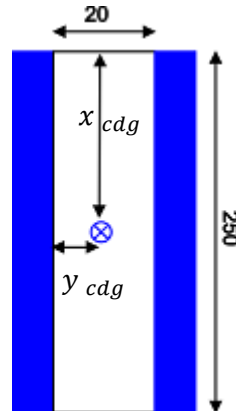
(1): Geometría de cordones de soldadura
